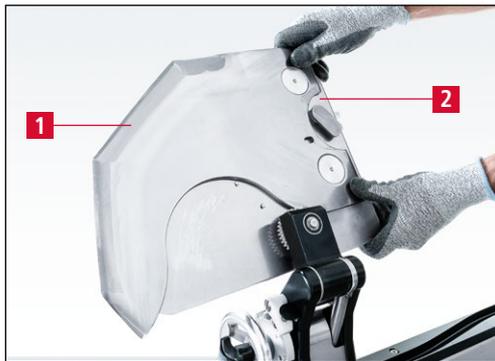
Serrage du couteau sur le plateau d'affûtage
